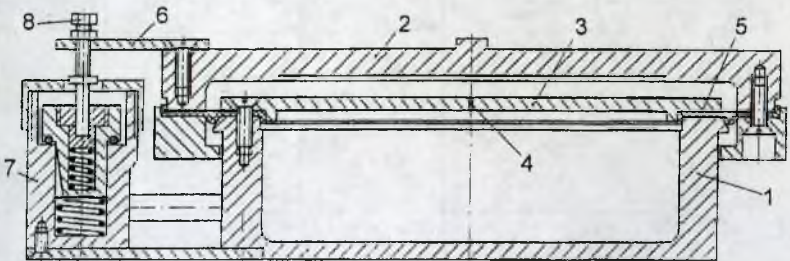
Конструктивная схема пневматической виброизолирующей системы: 1—корпус; 2—крышка; 3—перегородка; 4—межкамерный дроссель; 5—эластичная диафрагма; 6—рычаг обратной связи; 7—автоматический регулятор уровня; 8—регулируемый винт
